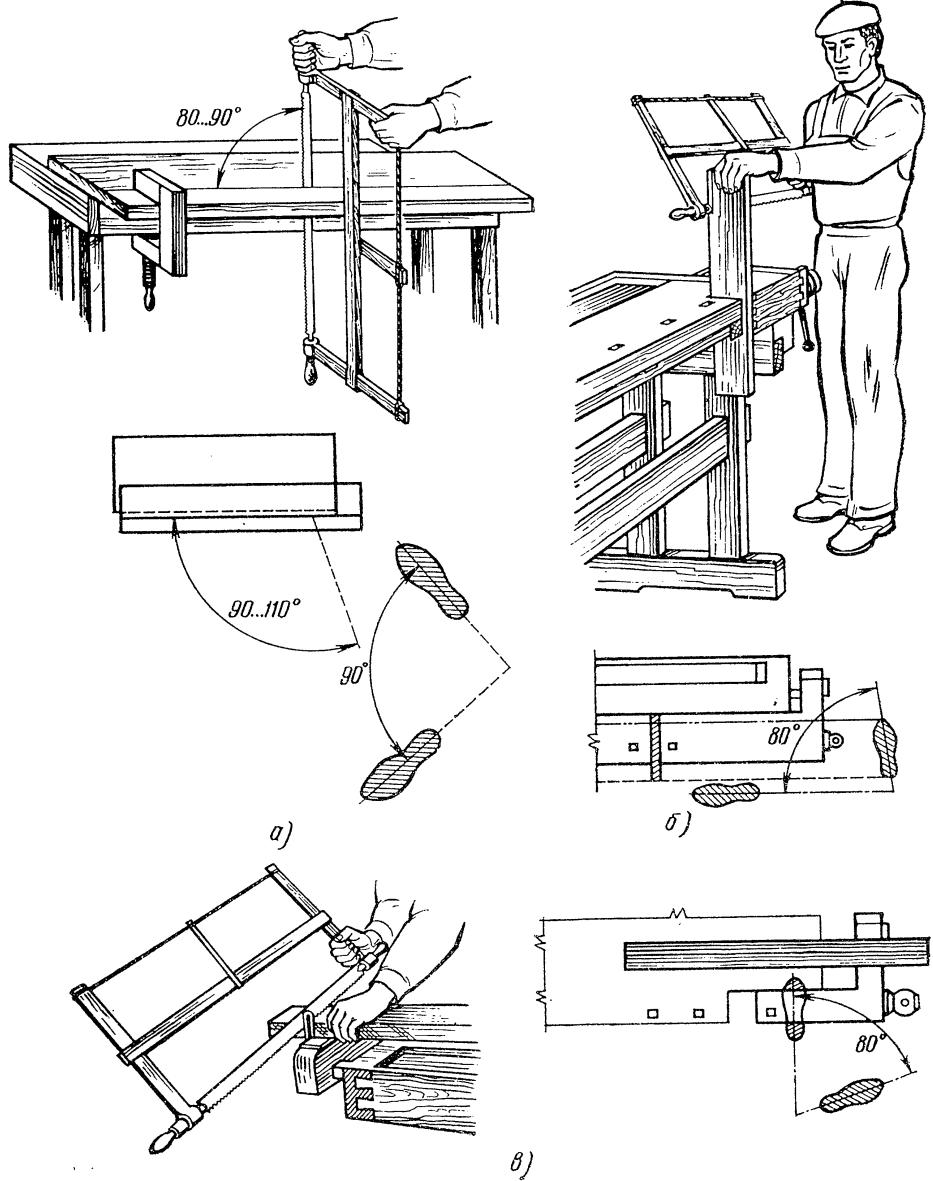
Приемы пиления лучковыми пилами и положения ступней ног рабочего при пилении:
